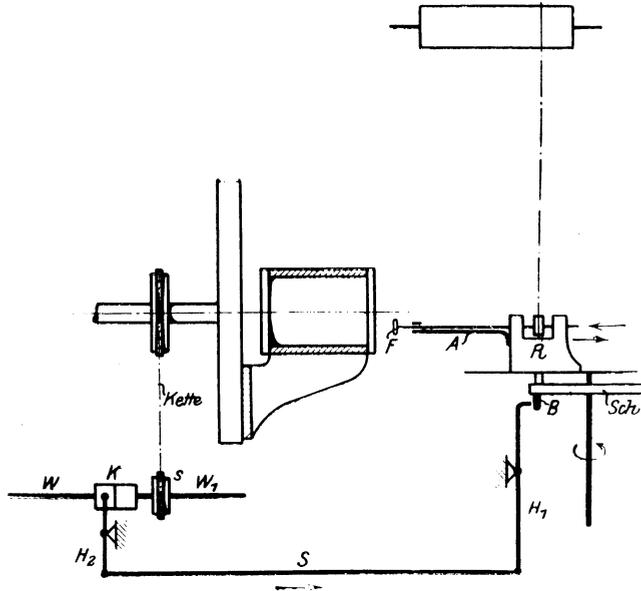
Einarbeiten der Schmiernuten auf einer Sonderfräsmaschine.
